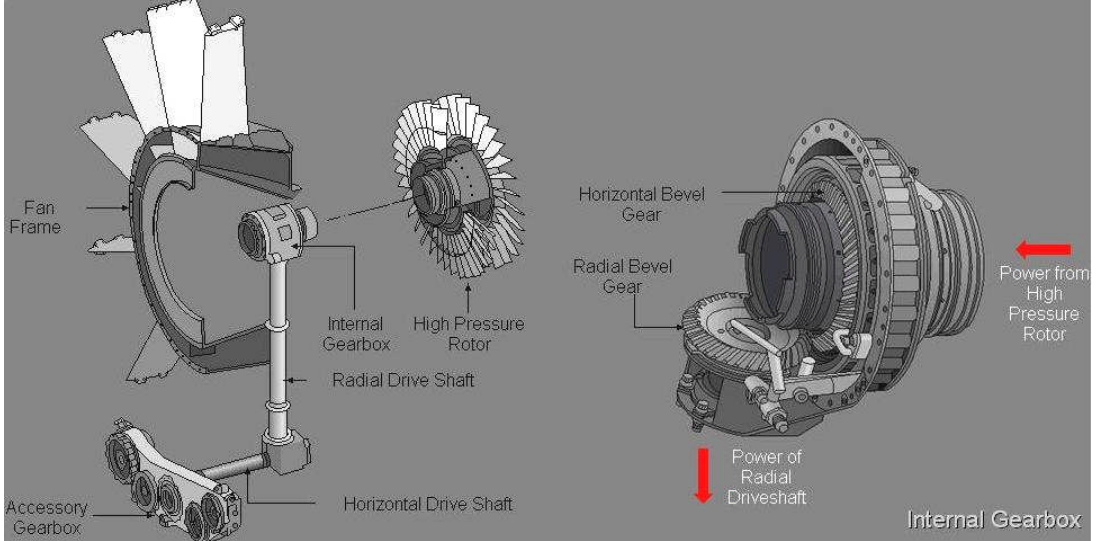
Alçak hız ve yüksek hız dişli kutularının motor şaftlarından güç iletimi şeması
